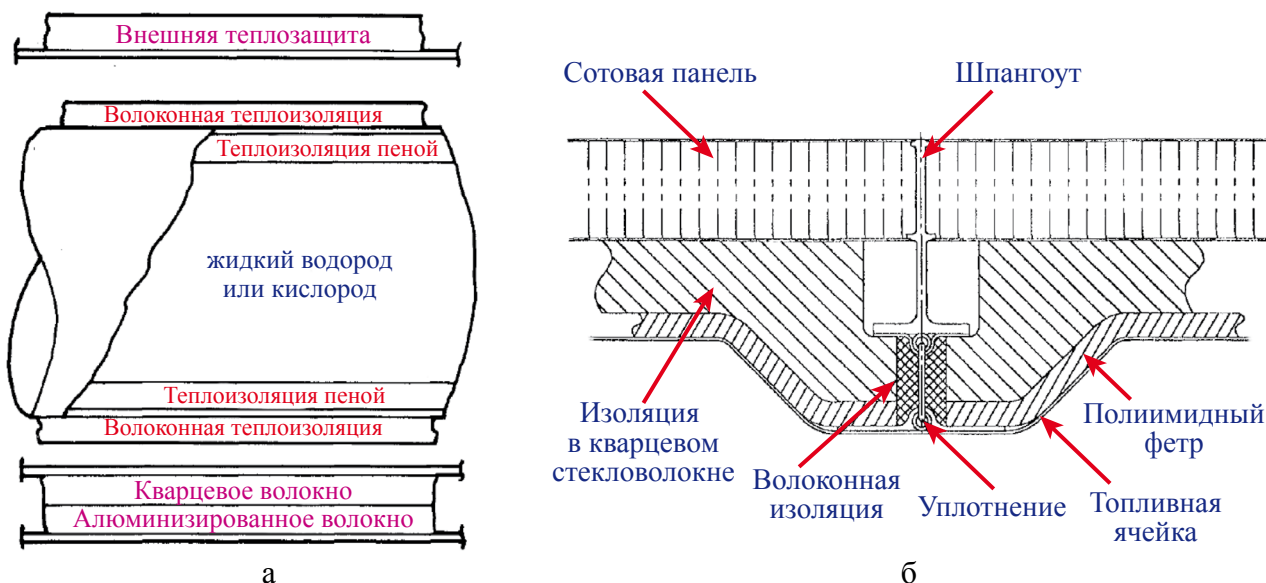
а – теплоизоляция бака с криогенным топливом, б – теплоизоляция бака с углеводородным топливом
